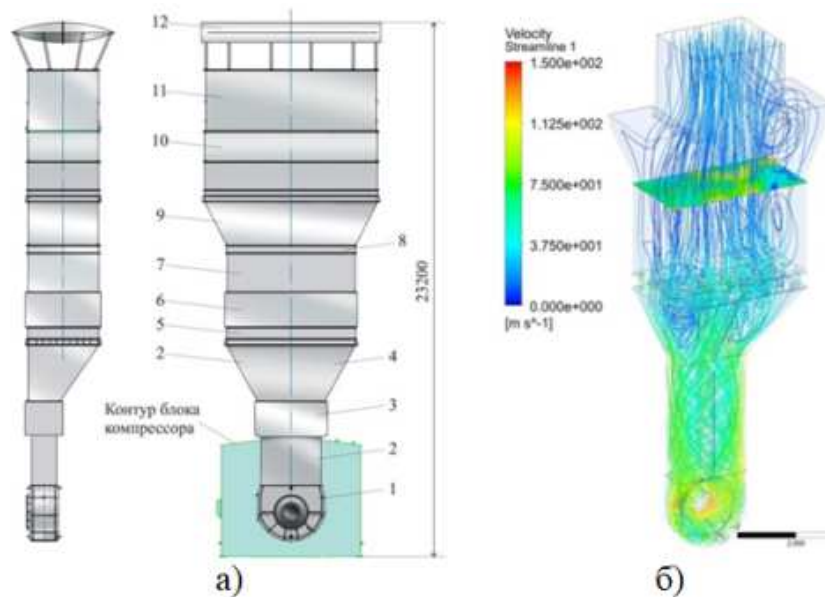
Конструктивная схема а) и линии тока б) в проточной части новой конструкции выхлопного тракта агрегата типа ГПА-Ц-16С: 1 – улитка; 2 – переходник улитки; 3 – компенсатор; 4 – диффузор 1-й ступени; 5 – выравниватель потока; 6 – компенсатор; 7 – проставка; 8 – СКОВ; 9 – диффузор 2-й ступени; 10 – утилизатор теплоты; 11 – шумоглушитель; 12 – зонт
